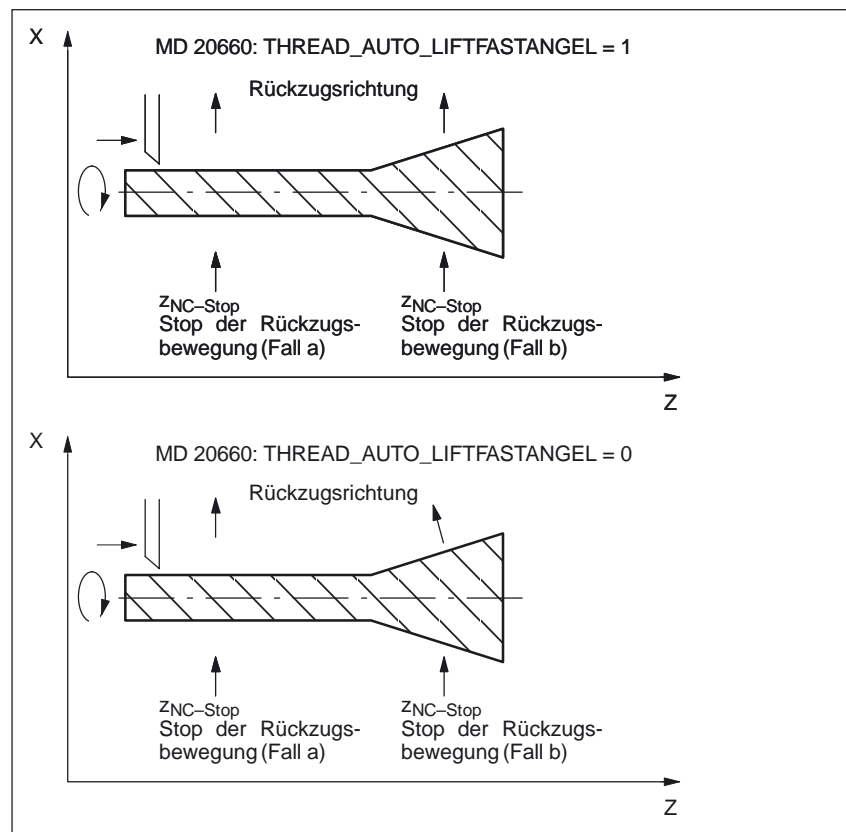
Rückzugsrichtung (Bearbeitung Außengewinde)
